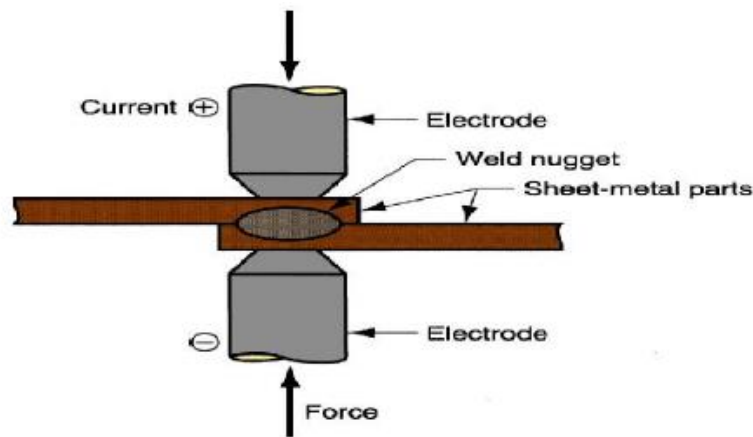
Representação Esquemática de uma Soldadura por Pontos
